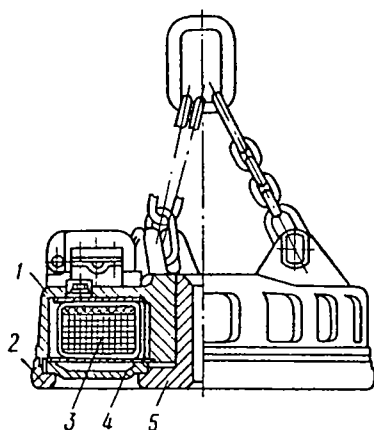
Электромагнитная шайба: 1 – корпус; 2 – наружный полюс; 3 – катушка; 4 – немагнитная шайба; 5 – внутренний полюс
